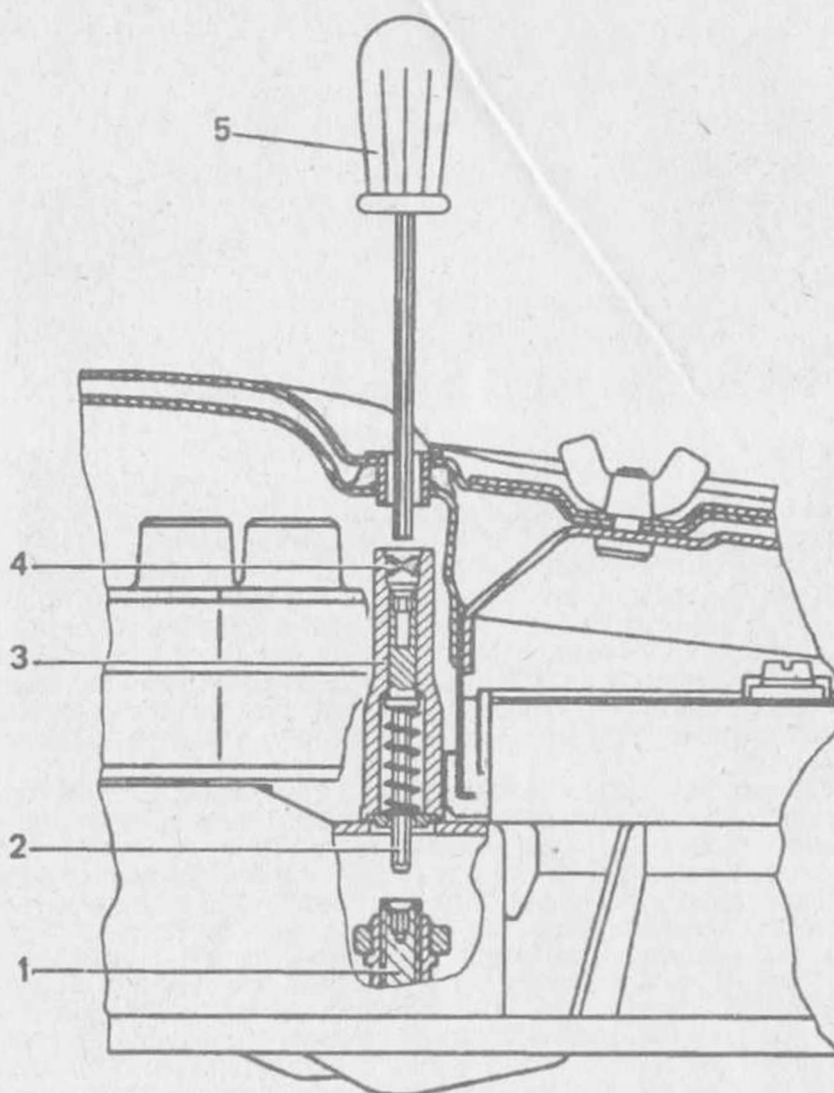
Регулировка содержания оксида углерода в отработавших газах: 1 — регулировочный винт; 2 — шток регулирующего устройства; 3 — регулирующее устройство; 4 — заглушка; 5 — отвертка
